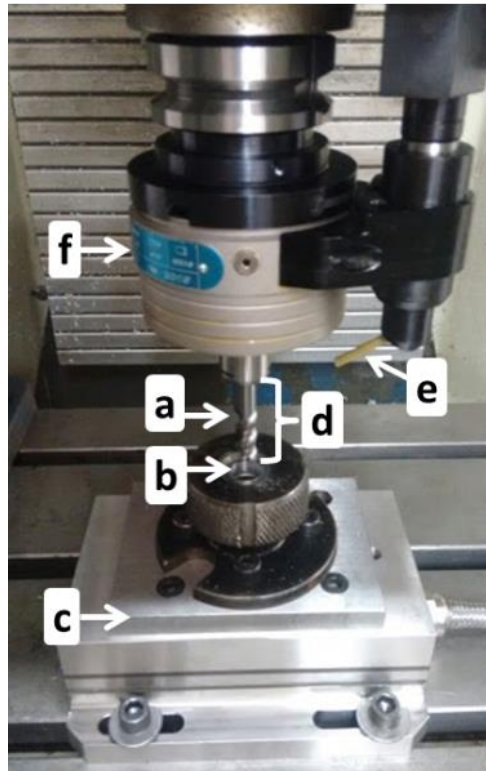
Centro de usinagem: ferramenta (a), corpo de prova (b), dinamômetro (c), comprimento em balanço (d), bico lubrificante (e) e multiplicador de rotação (f)
